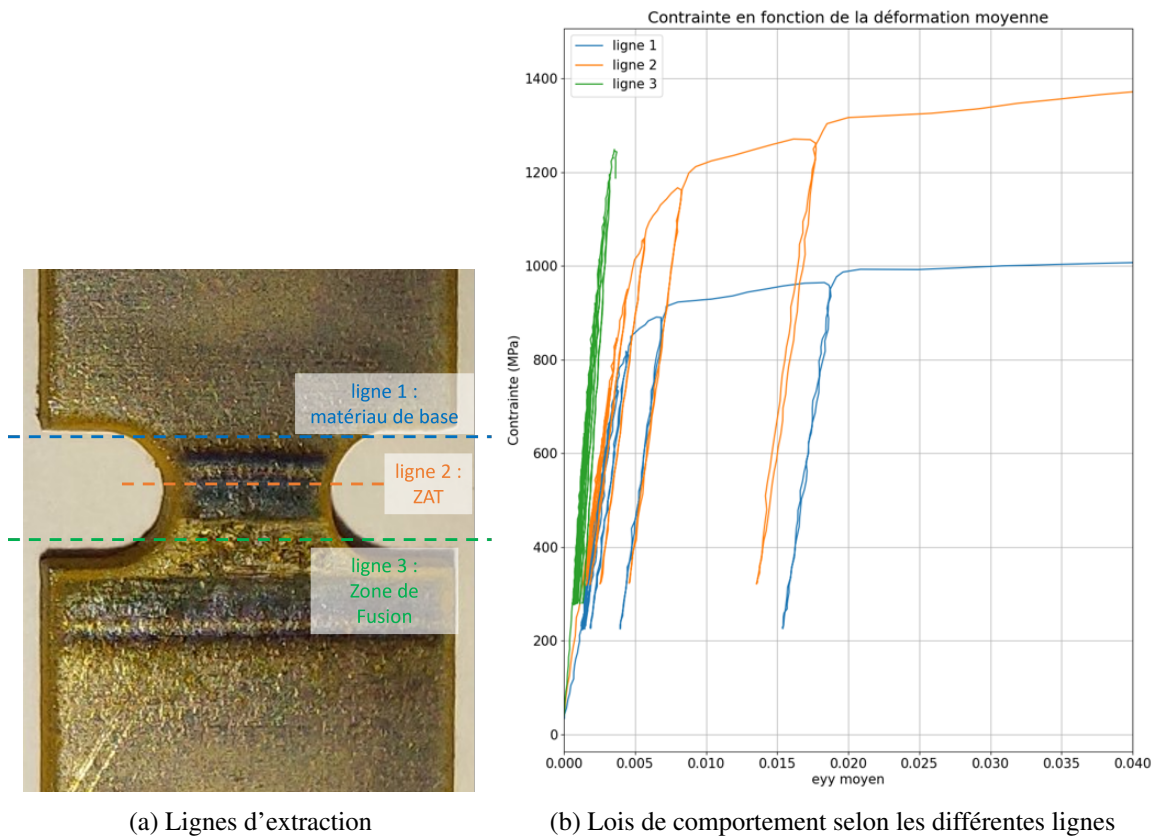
Lois de comportement des différentes zones de la soudure - éprouvettes à encoches larges avec soudure
